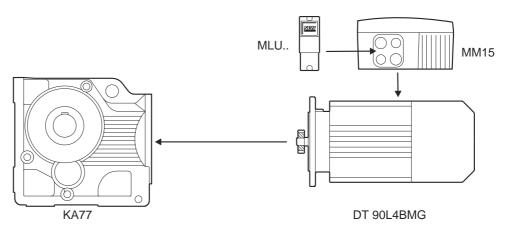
Beispiel für die Typenbezeichnung MOVIMOT®-Getriebemotor
